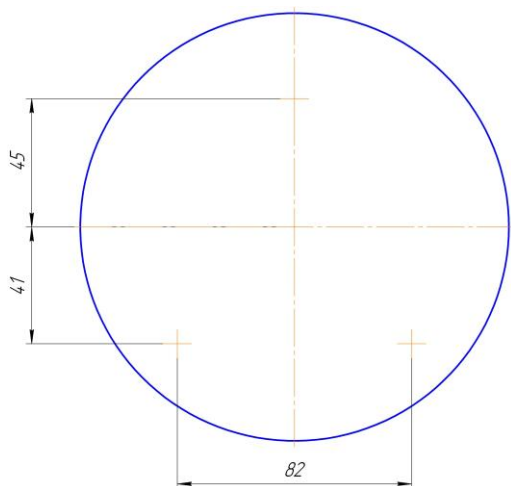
Размеры для крепления установки ПУЗП 2.1 к столу
